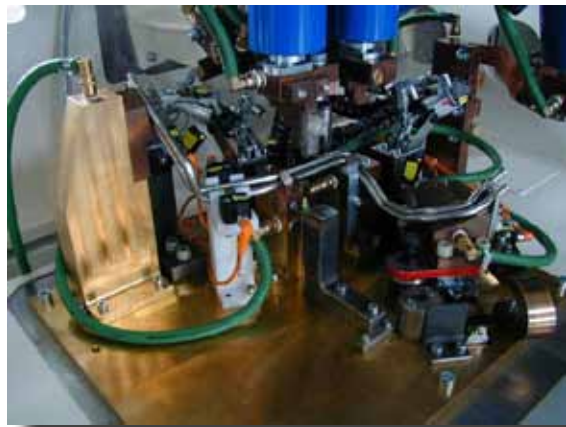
Widerstands-Schweißvorrichtung
